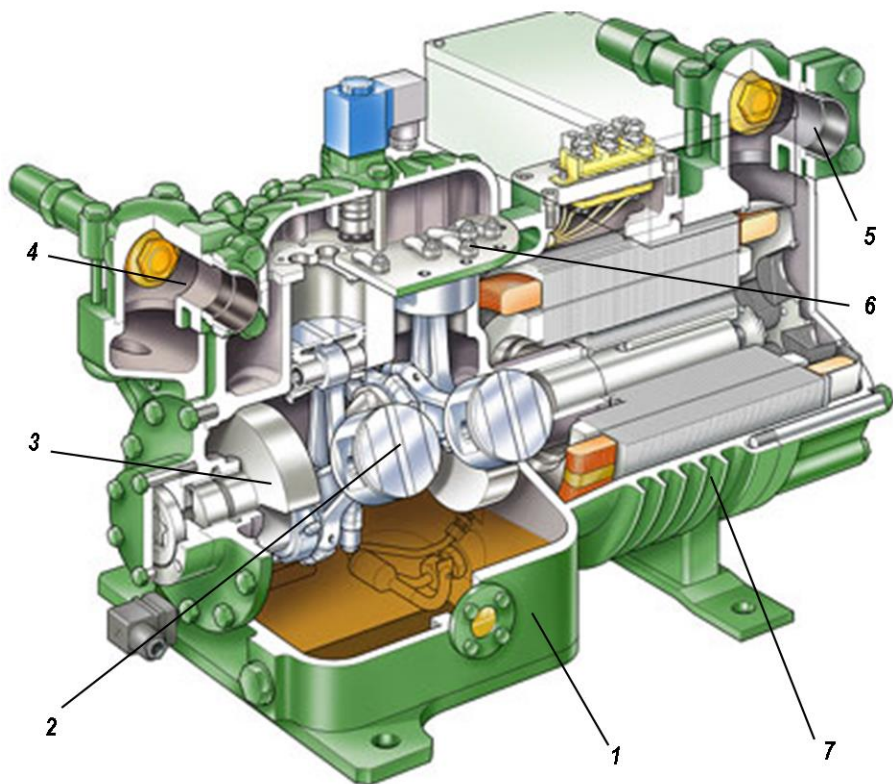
Компресор в розрізі: 1 – корпус ; 2 – поршень; 3 – колінчатий вал; 4 – нагнітаючий патрубок; 5 – патрубок всмоктування; 6 – клапани; 7 – електродвигун
